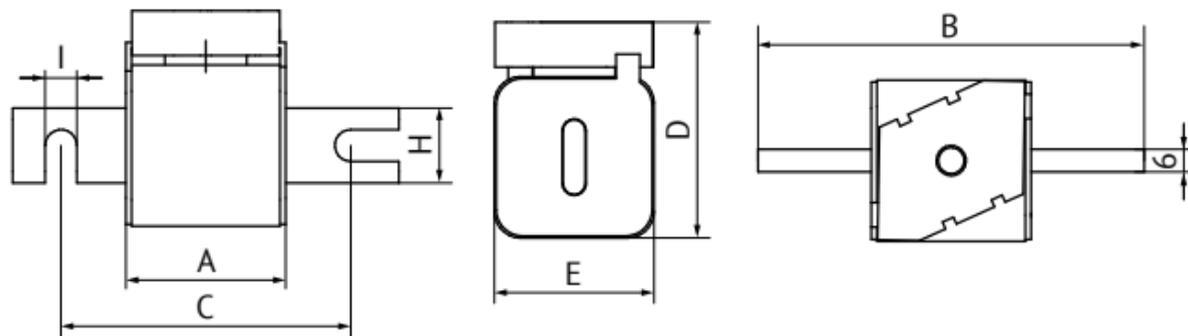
Размеры для габаритов S30, S31, S32, S33
